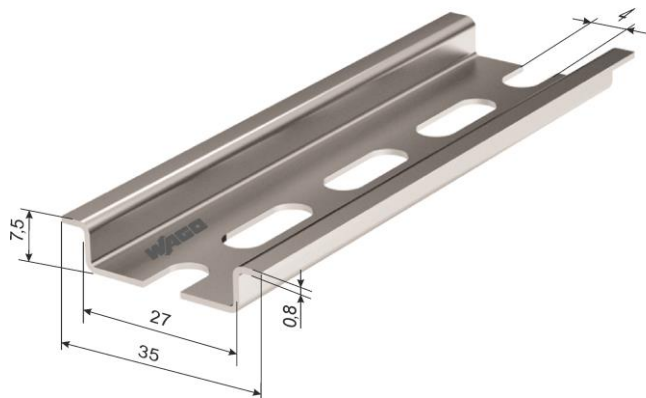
Внешний вид и размеры DIN-рейки Wago
